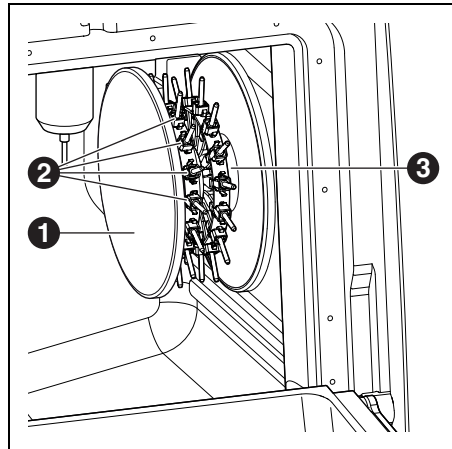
Übersicht Werkzeuglager (Tool Blank) im ausgefahrenen Zustand
